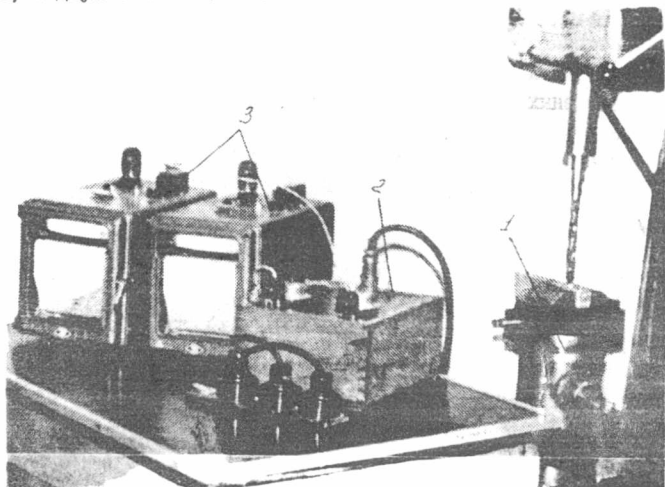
Общий вид установки для измерения силы подачи и крутящего момента при сверлении
